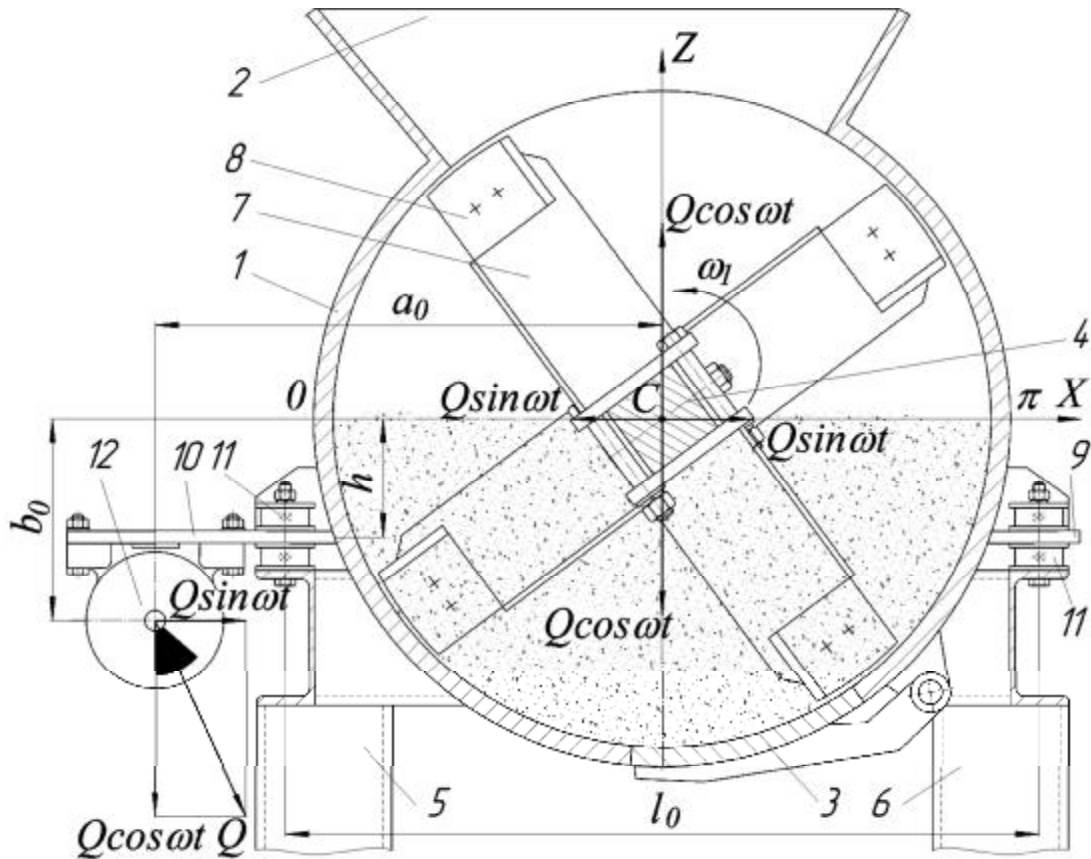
Расчётная схема бетоносмесителя принудительного действия с осциллирующими колебаниями корпуса: 1 – корпус смесителя; 2 – загрузочная коробка; 3 – люк; 4 – лопастной вал; 5, 6 – стойки рамы; 7 – центральная лопатка; 8 – периферийная лопатка; 9, 10 – кронштейны; 11 – упругие амортизаторы; 12 – вибровозбудитель колебаний
